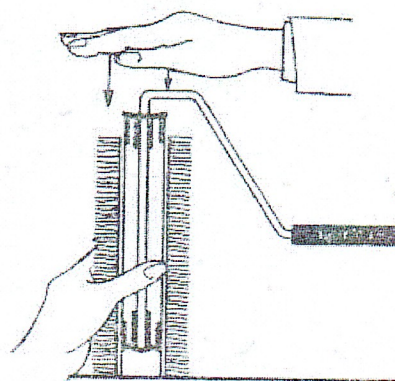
Modul de introducere a axului și a capacelor-lagăre în tubul cilindrului rolei.
